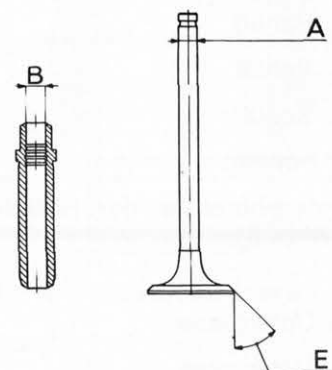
Hauptabmessungen der Ventile und Ventileführungen.
